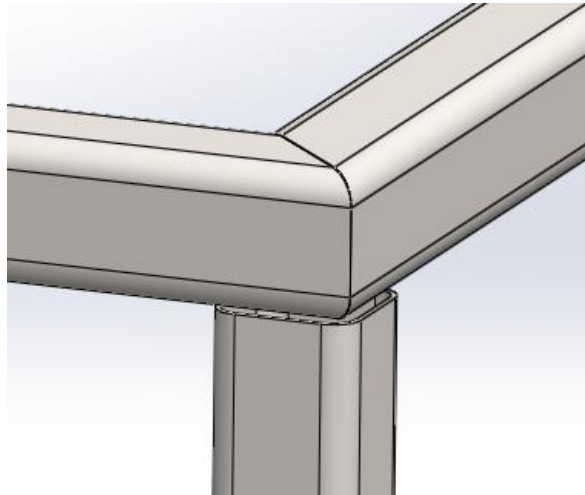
Detalle juntas soldadas (Esquina)
